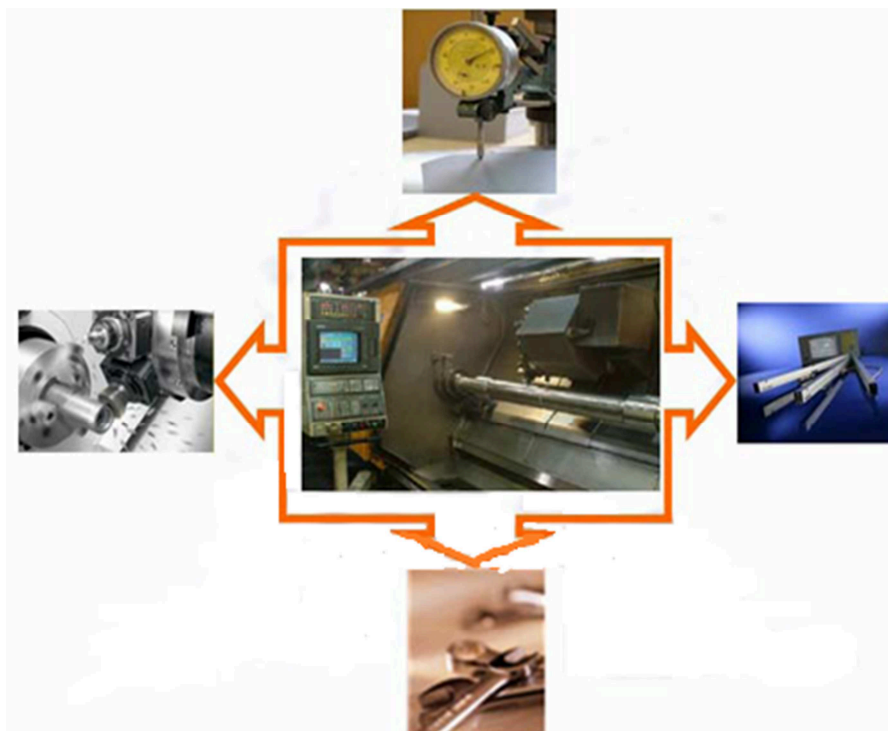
Příklad komplexního přístupu u CNC obráběcího stroje [1]
